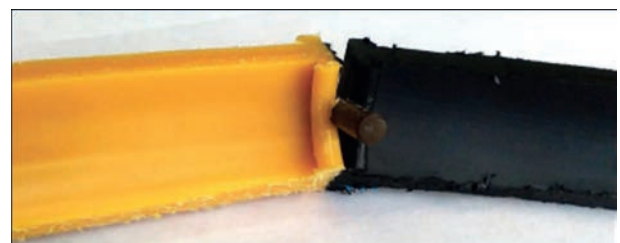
Зразок стикового зварного з'єднання поліетиленових труб, зруйнований після випробувань
